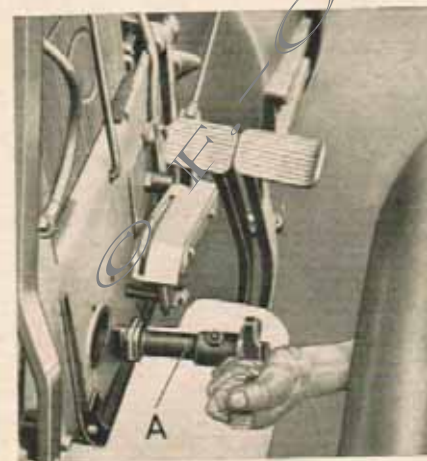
Das Mäherschaltgehäuse (A) mit eingebauter Schaltwelle wird am Fußhebel gelöst und in das Rundloch des Getriebegehäuses eingeschoben.
